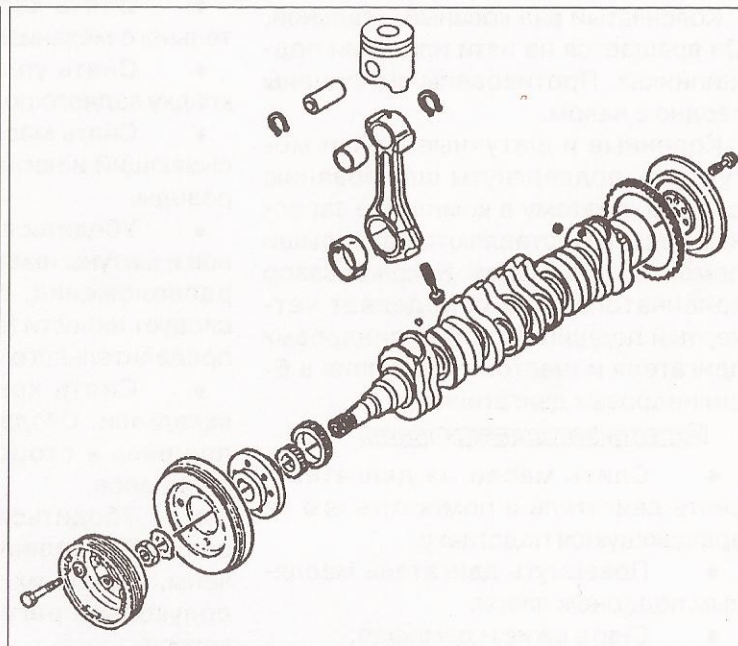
Подвижная система 6-цилиндрового двигателя
